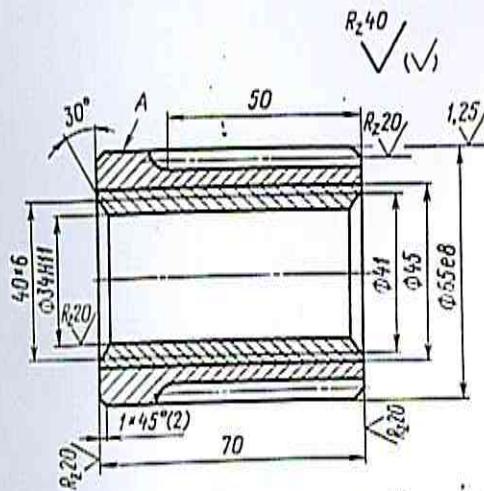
Гайка биметаллическая. Деталь 6М82.7.101
